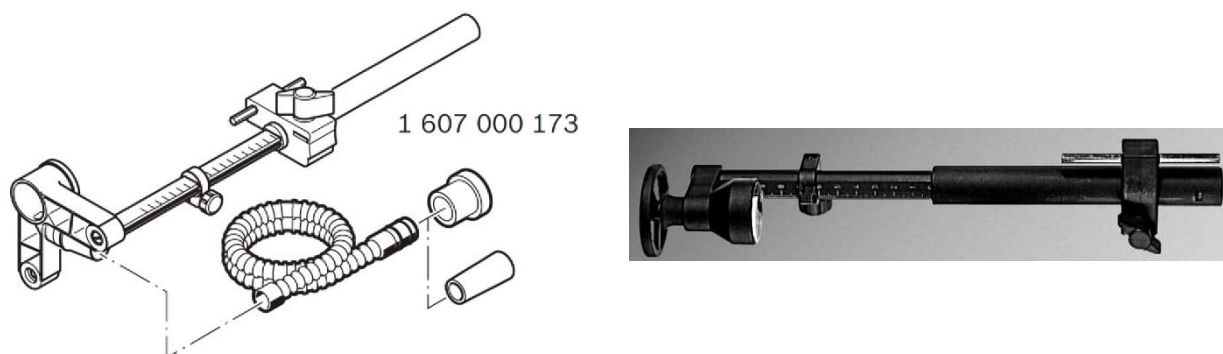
Угломер (контроллер угла сверления) с устройством для вывода пыли
